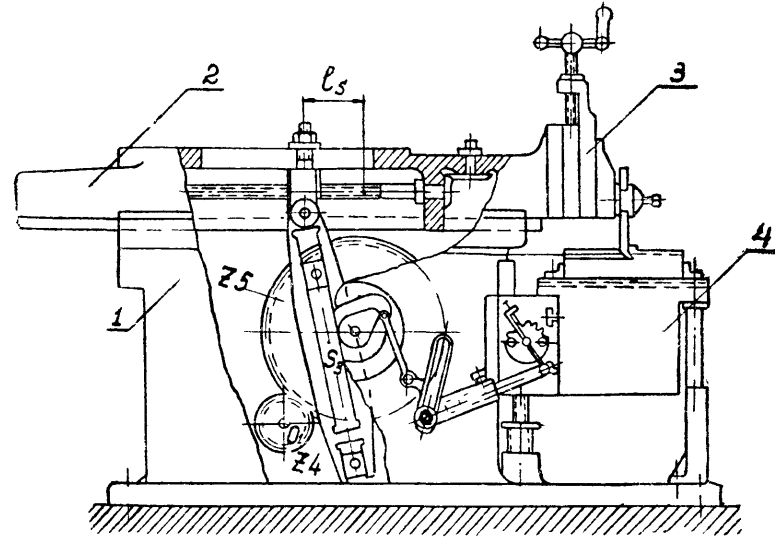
1 Общий вид поперечно-строгального станка с качающейся кулисой
